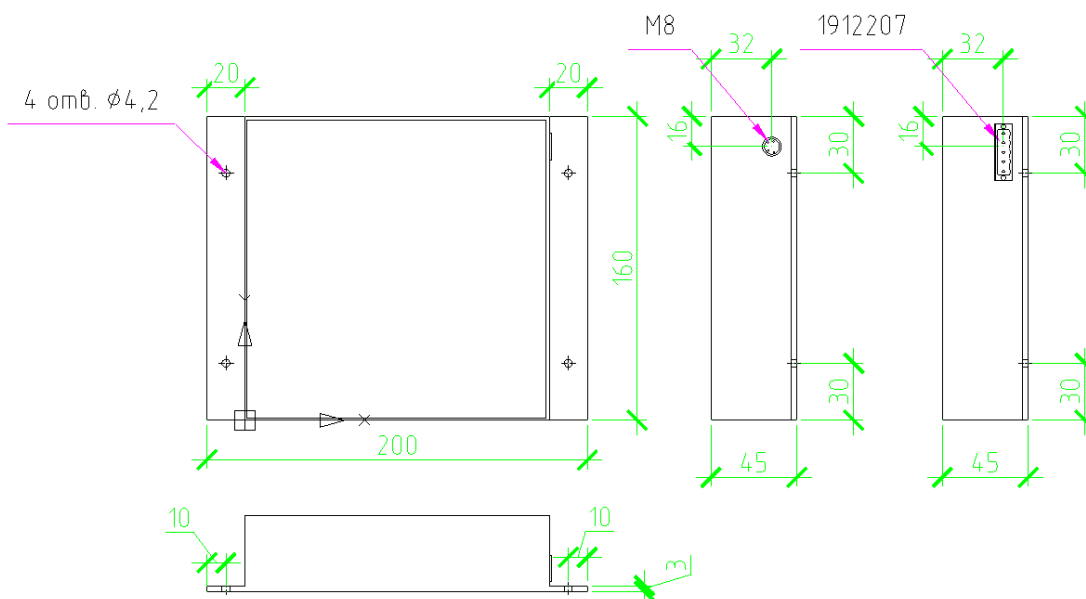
Габаритные размеры модуля в полиуретановом корпусе (2 варианта)
